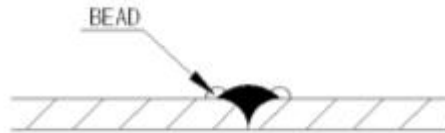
수동용접(hot air welding 상세도)
